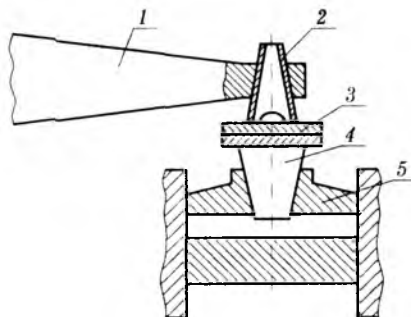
Схема контурной ультразвуковой сварки:
